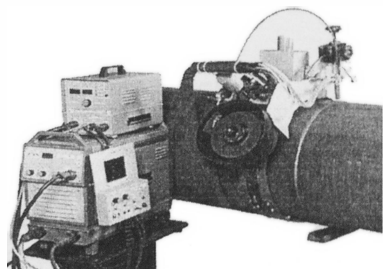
Установка для орбитальной сварки УАСТ-1 НПП «Технотрон»
